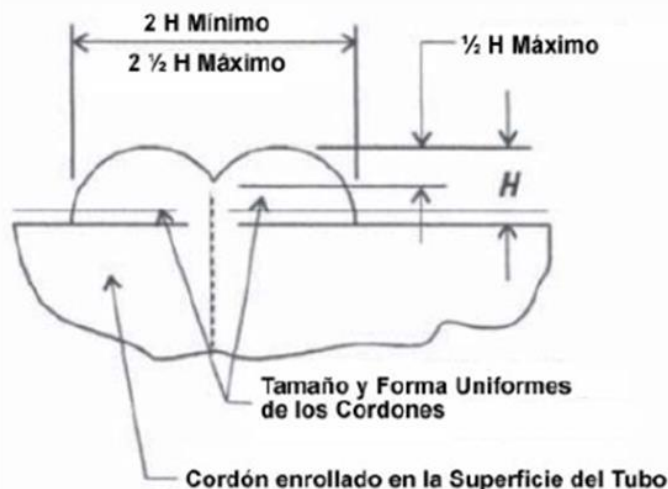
Esquema de cordón de soldadura aceptable
